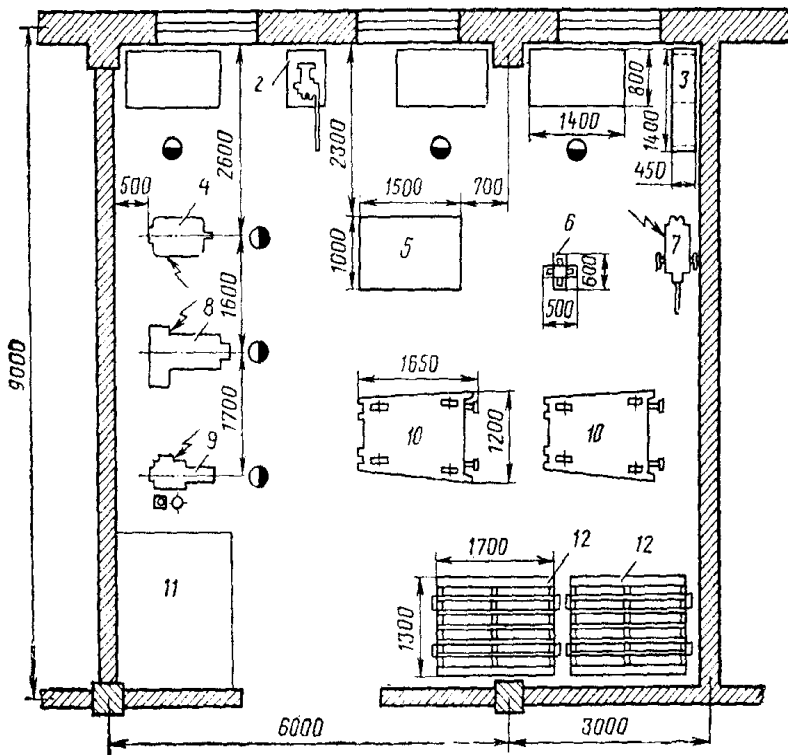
Технологічне планування бляхарського відділення: 1 — верстаки; 2 — ножиці; 3 — стелаж; 4 — станок вертикально-свердильний; 5 — плита рівняльна; 6 — стенд для ручного рихтування; 7 — станок шліфувальний; 8 — зиг-машина; 9 — установка для зварювання; 10 — візок-стенд для ремонту кабін; 11 — місце для зберігання листового матеріалу; 12 — стелажі для крил
